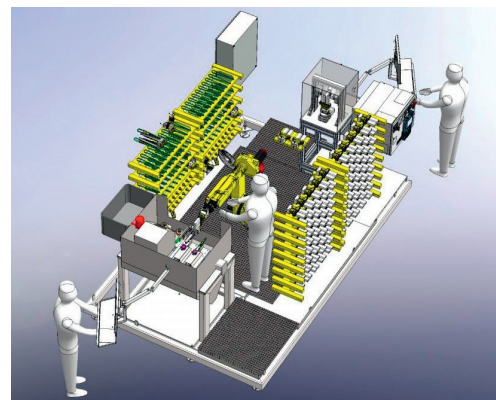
Комплекс адаптивной шлифовки и полировки лопаток
